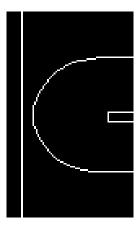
Dibujo del cono de entrad del motor Makila 1A
